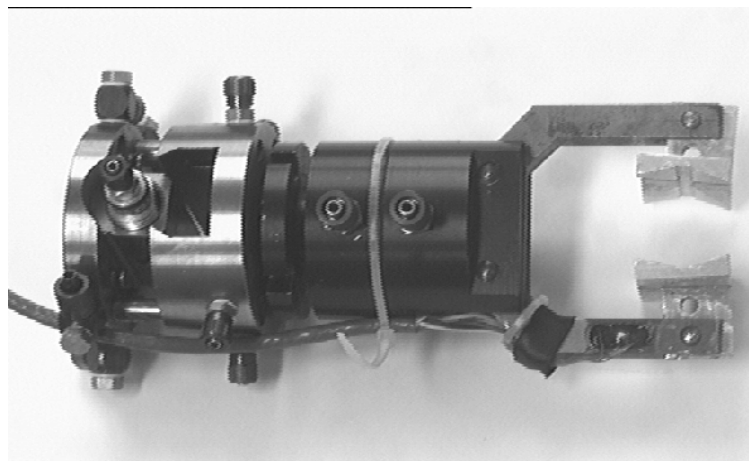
Werkzeugwechsler (links) und Robotergreifer mit Kraftmeßfinger
